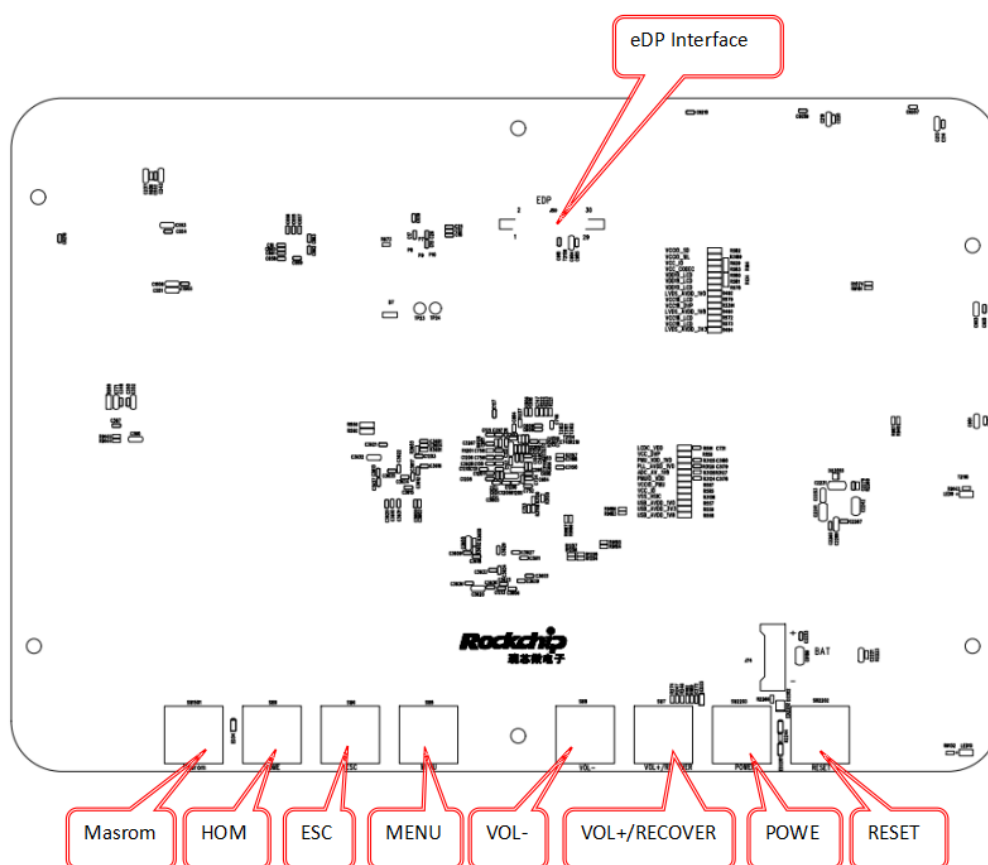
RK3288 EVB 2.0 PCB 上 bottom Layer 模块布局位置图
